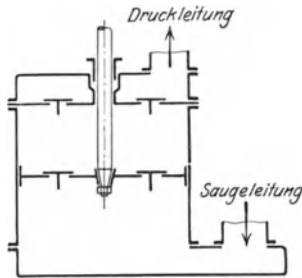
Schema einer stehenden Naßluftpumpe mit Kolbensaug- und Druckventilen.
